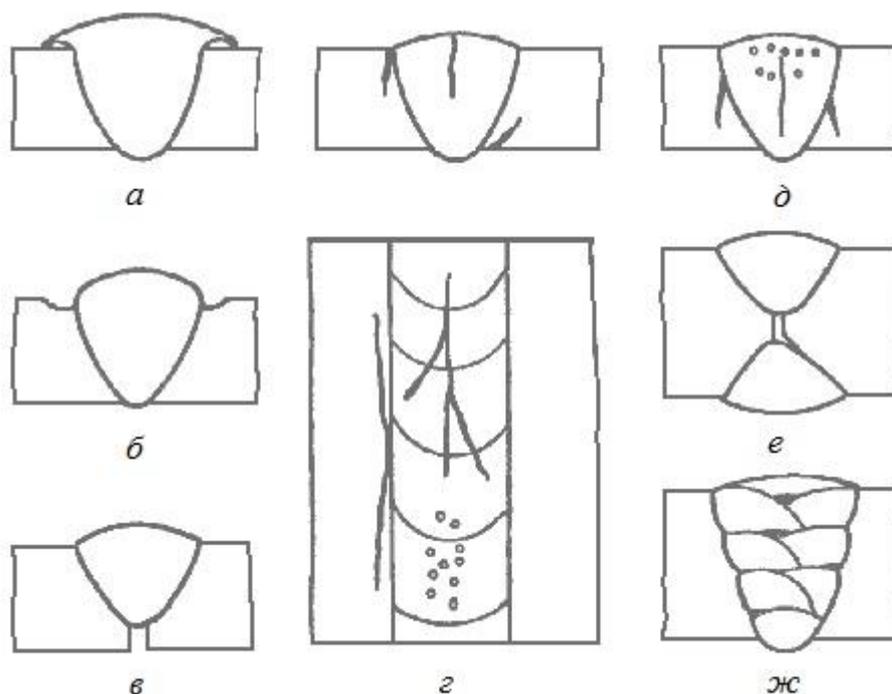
Виды дефектов в сварных соединениях
